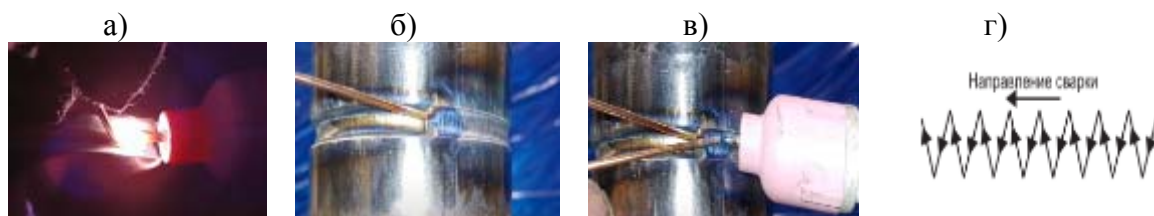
Способ выполнения сварки трубного образца в горизонтальном положении:
